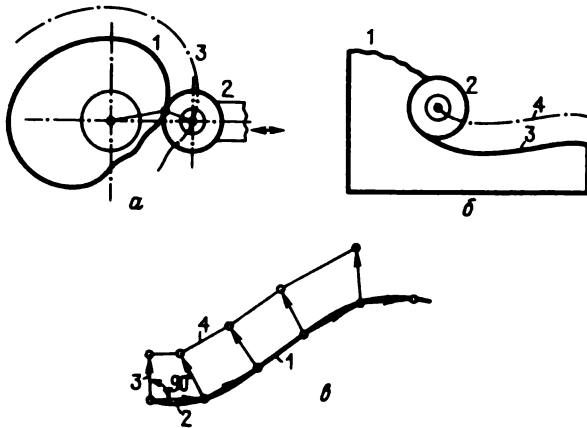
Применение эквидистант: *a* – при расчете кулачкового механизма (1 – кулачок, 2 – роликовый толкатель, 3 – эквидистанта к профилю кулачка, определяющая движение центра ролика); *б* – для обработки деталей вращающейся фрезой (1 – заготовка, 2 – фреза, 3 – обрабатываемый профиль, 4 – эквидистанта к профилю, по которой движется центр фрезы); *в* – упрощенный численный способ построения эквидистант (1 – исходная кривая, 2 – вектор-хорда, аппроксимирующая касательную к кривой, 3 – вектор, нормальный к хорде, 4 – ломаная, аппроксимирующая эквидистанту)
